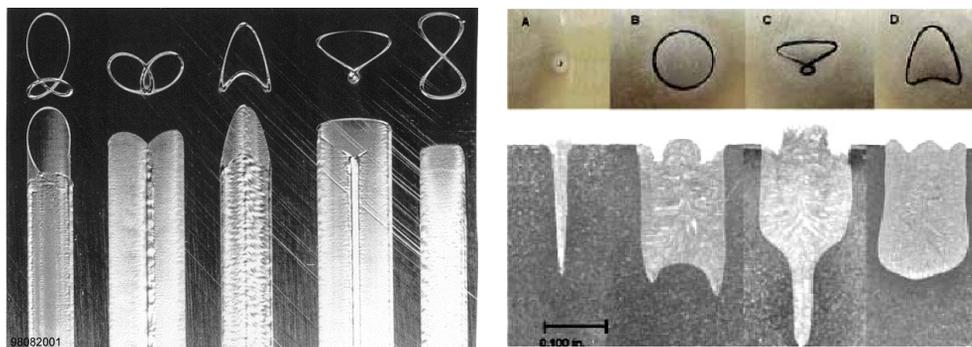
Влияние развертки электронного луча при осцилляции на форму сварного шва [3]
